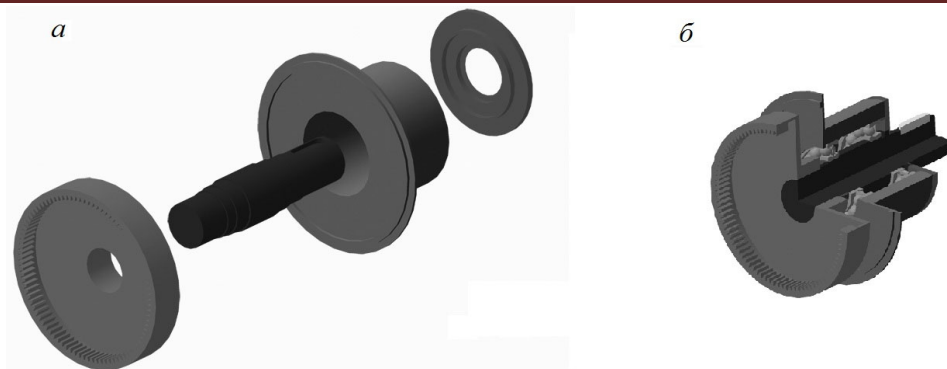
Комп’ютерні моделі деталей зубчастого колеса – епіцикла, введеного вала, елементів корпуса
